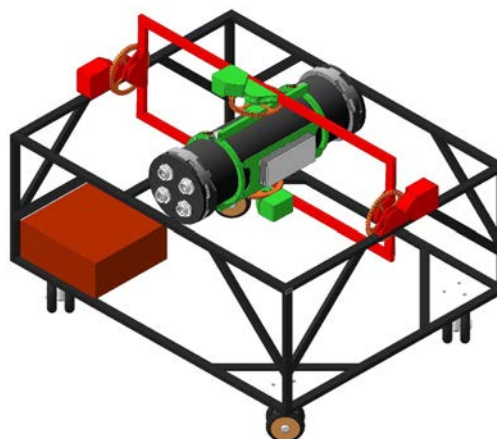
3D модель кріплення міцного корпусу 1) – капролонова основа; 2) – поворотні хомути; 3) – підшипникові опори; 4) – талрепи; 5) – полиця для розміщення портативного джерела живлення
